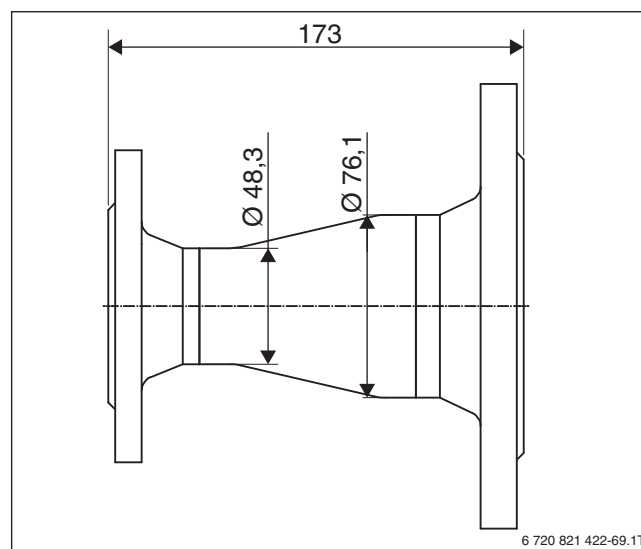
ábra Közdarab DN 65/PN 6 – G 1 ½ " (méretek mm-ben)
